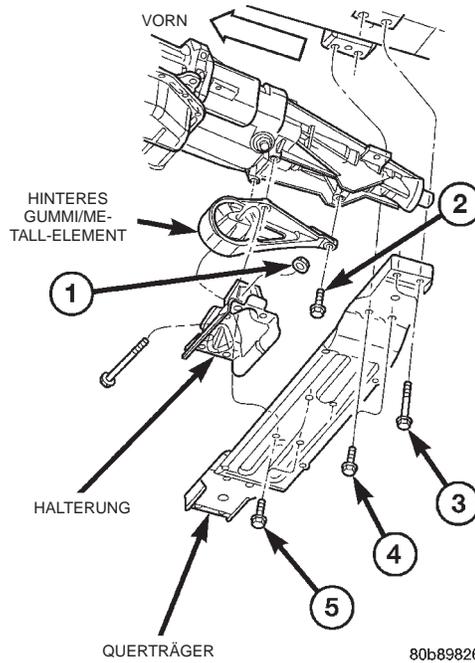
Hintere Motoraufhängung—Heckantrieb
